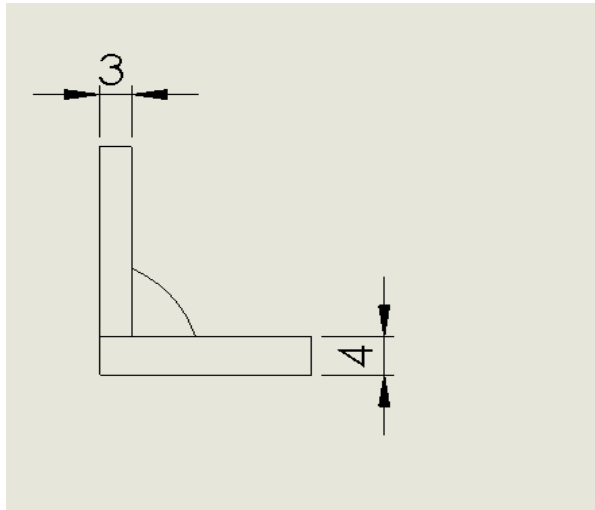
Diseño de junta soldada para placas de 3mm y 4mm. Fuente:
